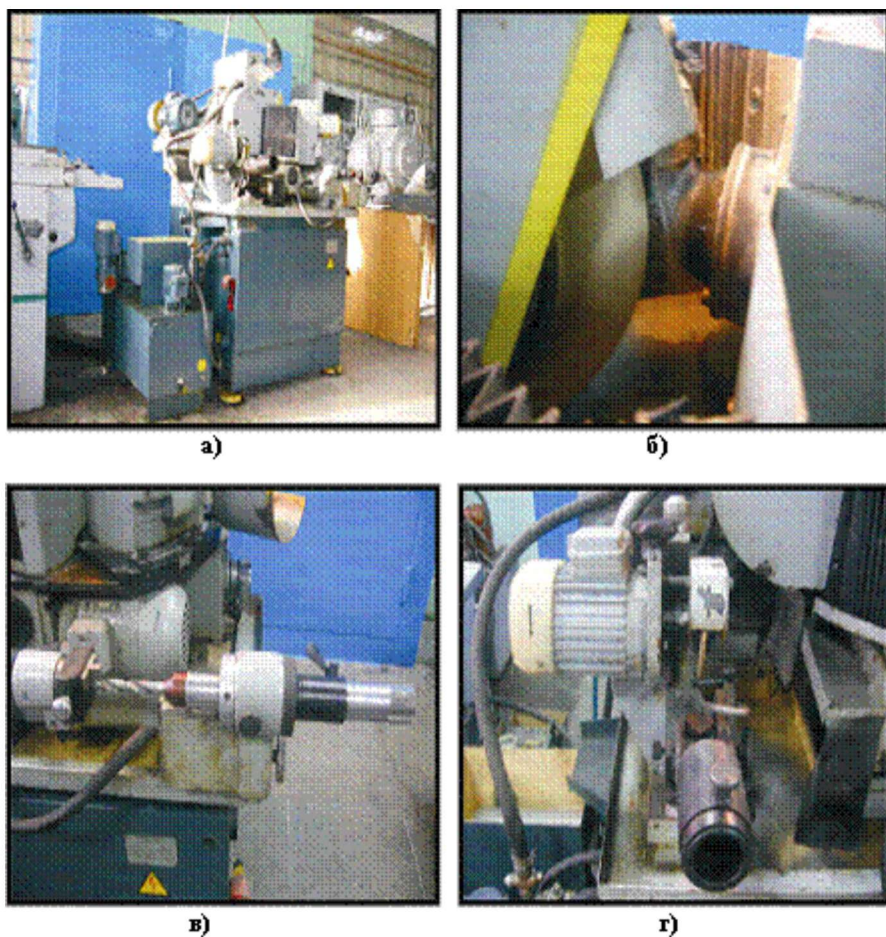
Общий вид полуавтомата заточного для сверл, зенкеров и метчиков модели ЗЕ653: *a* – общий вид полуавтомата с приспособлениями; *б* – зона затыловки задней поверхности инструмента; *в* – приспособление для базирования инструмента в патроне; *г* – механизм подточки поперечной кромки
